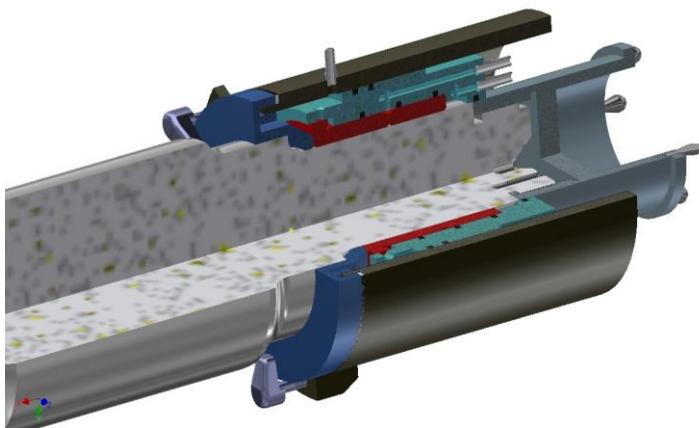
3D модель устройства для распрессовки колец буксовых подшипников колёсных пар
